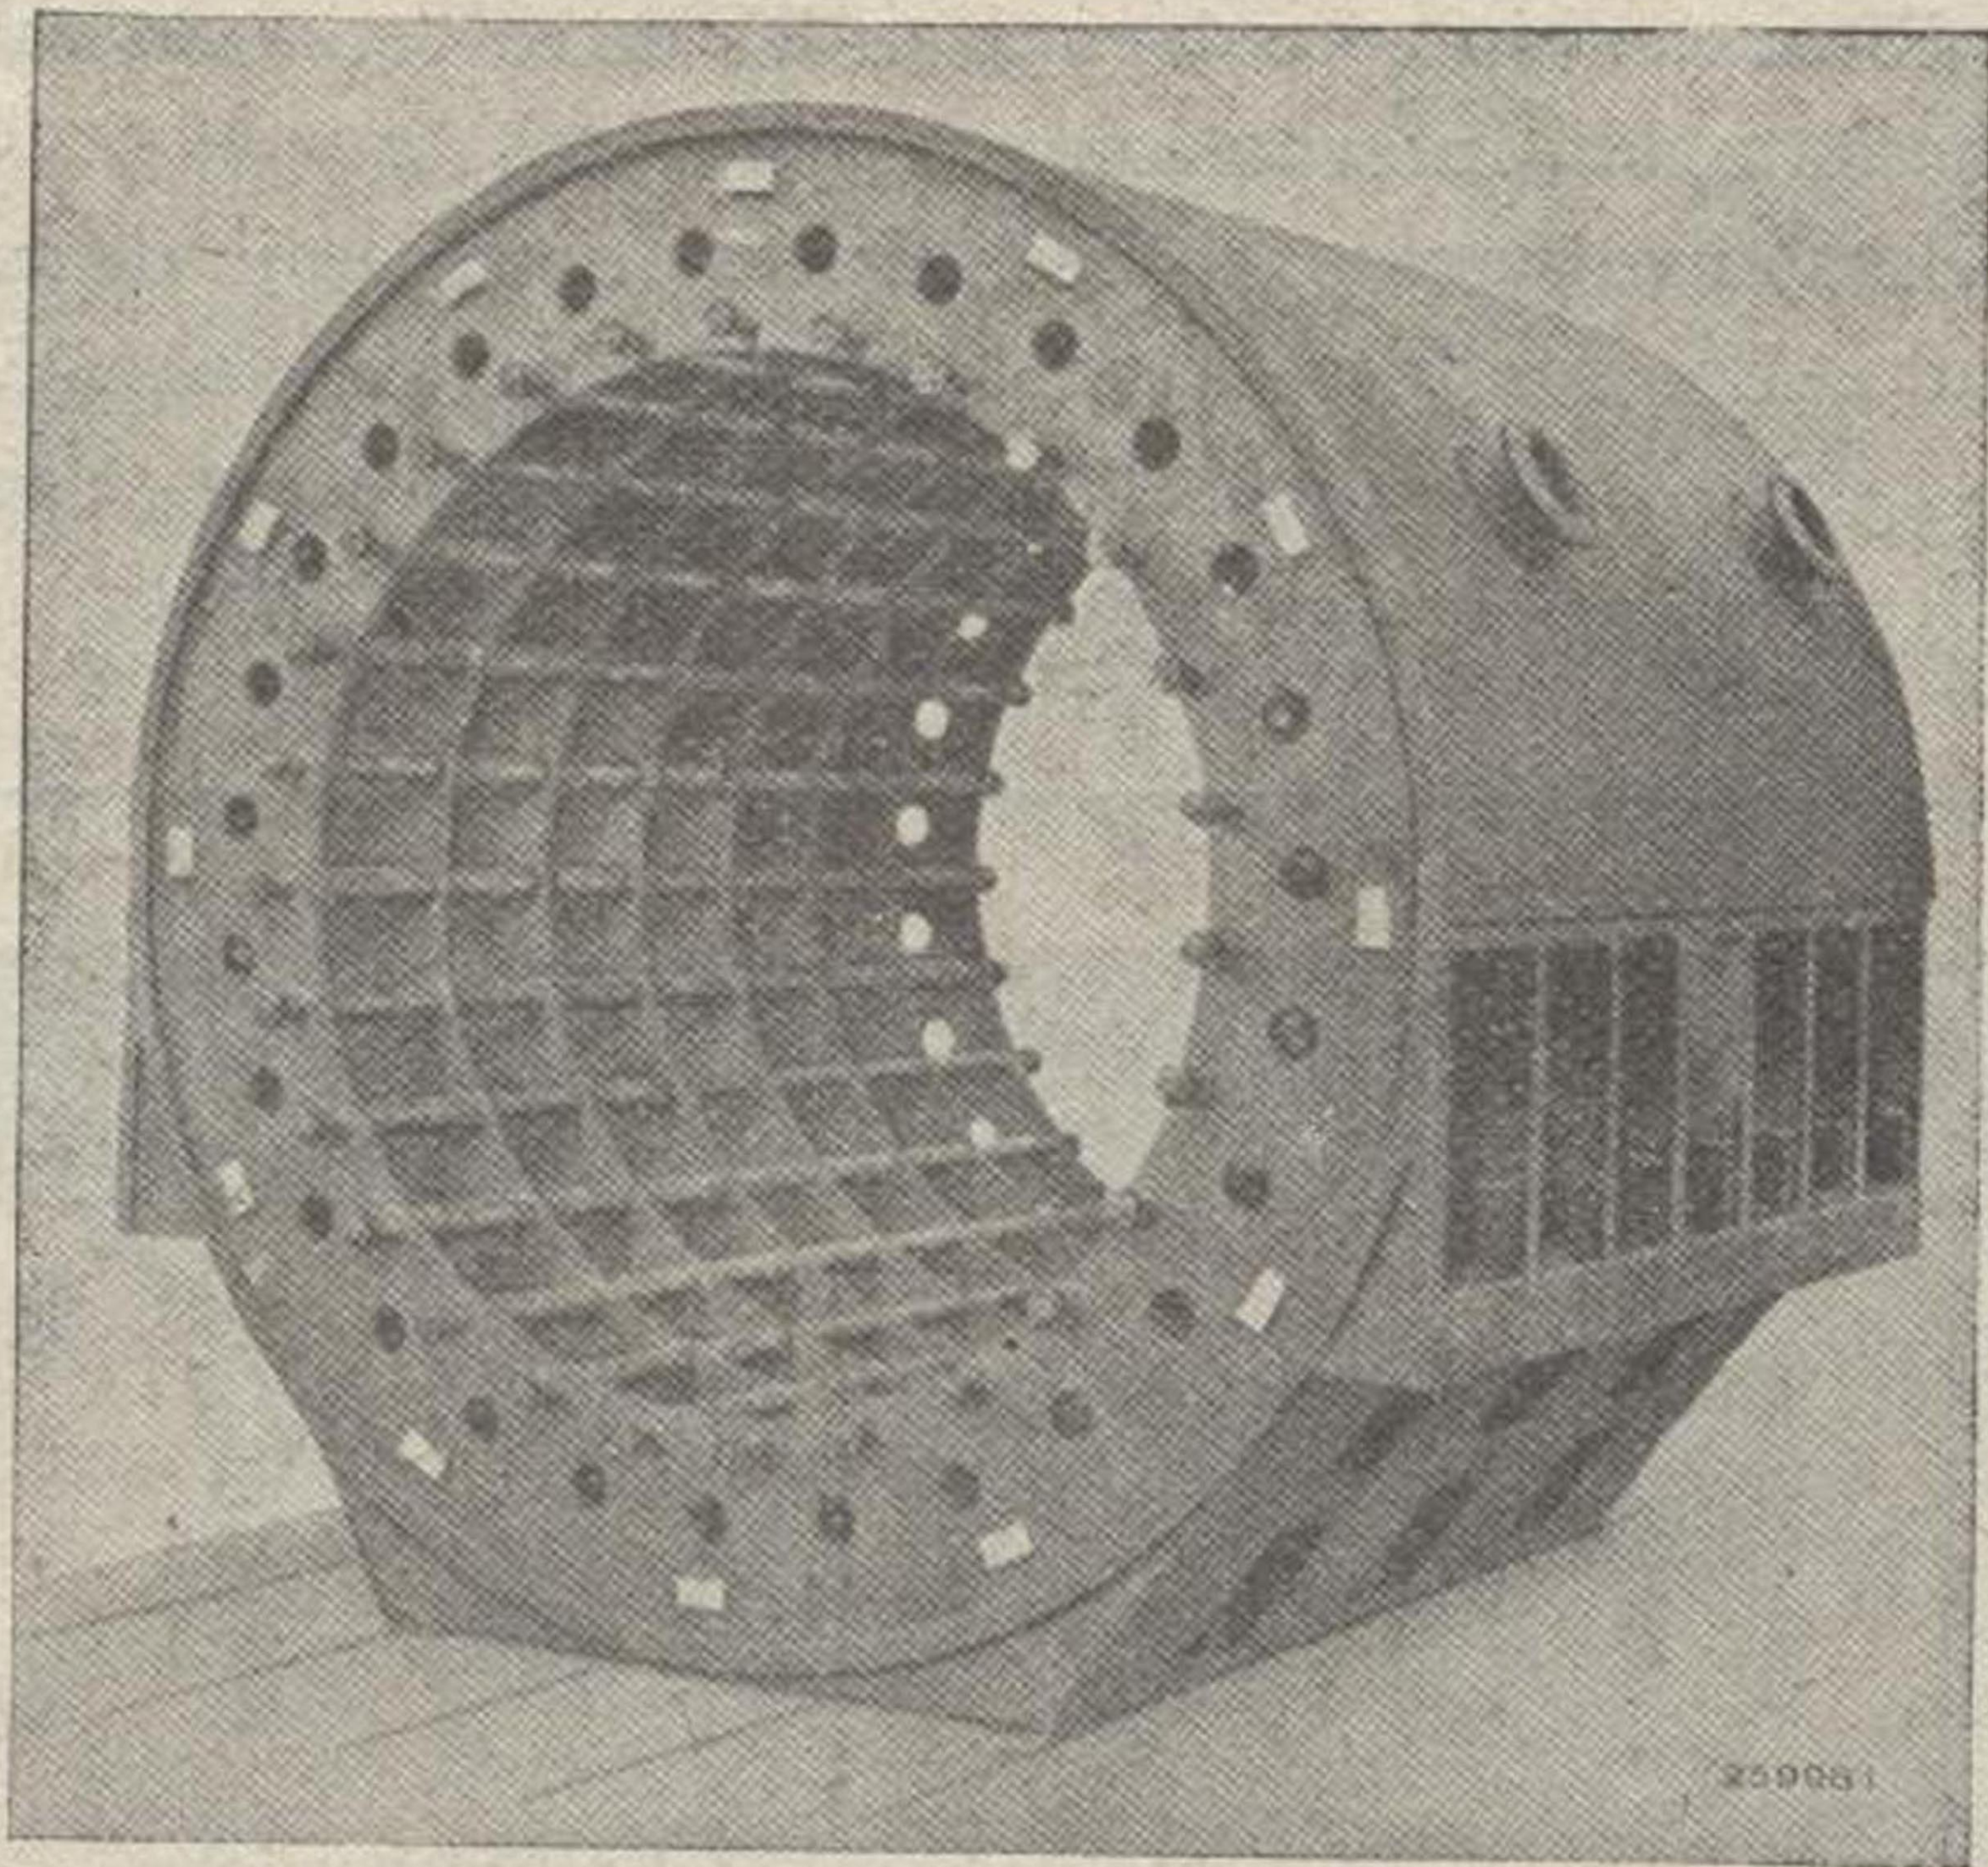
<sup>a</sup>—Carcasa de turboalternador de placas de palastro soldadas.
